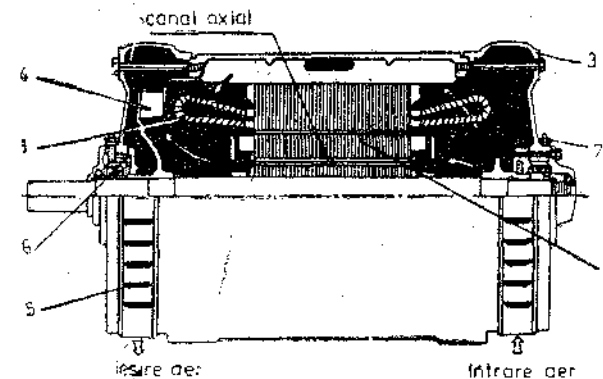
Motor asincron cu rotorul în scurtcircuit cu autoventilație axială, protecție IP 23:
